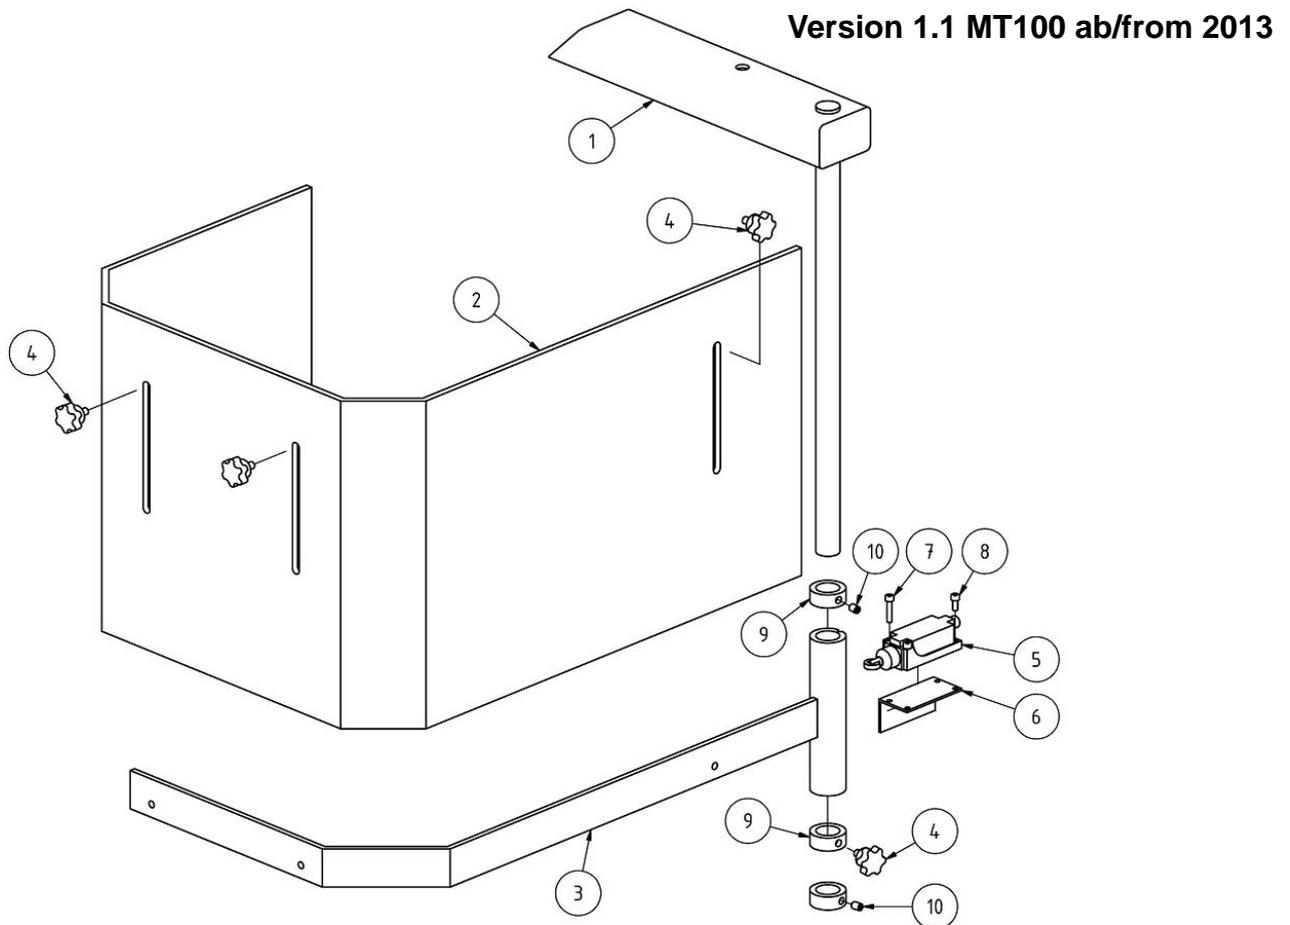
Fräsfutterschutz - Milling chuck protection
